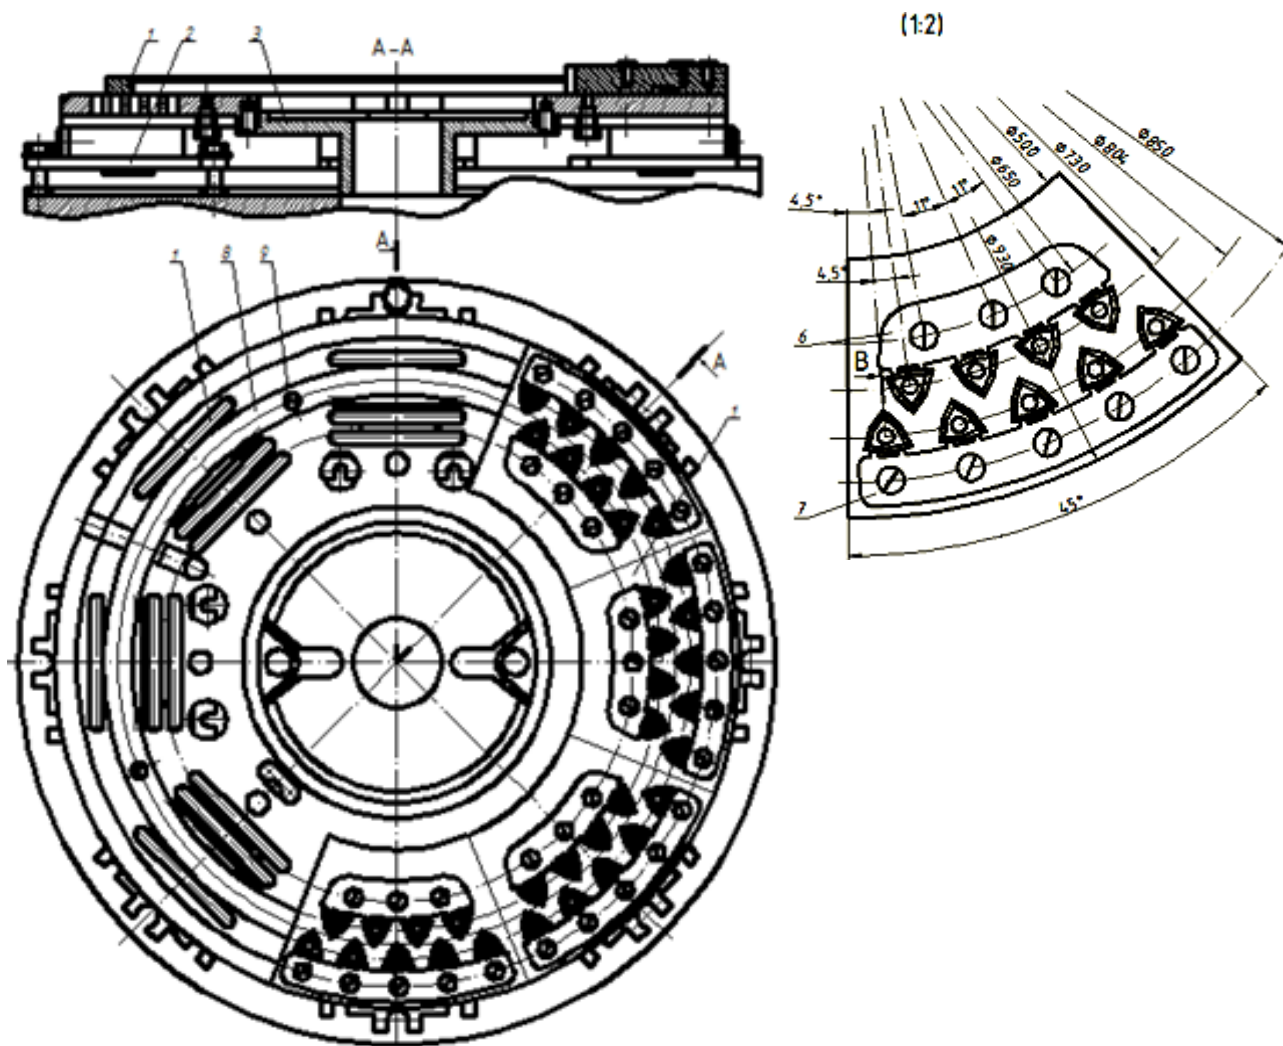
Приспособление для закрепления твердосплавных пластин при плазменной обработке
